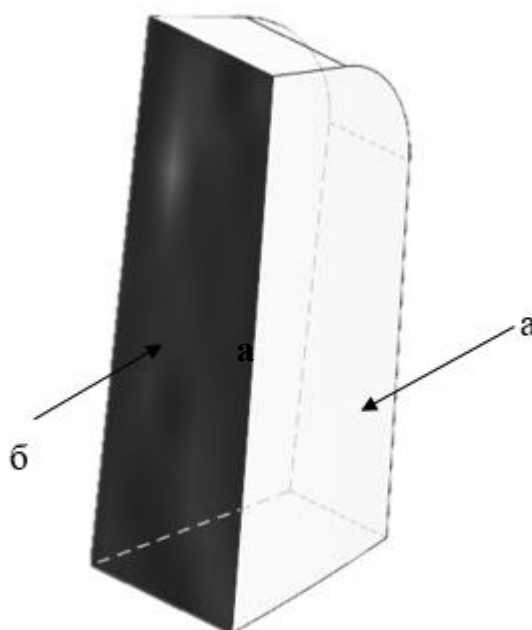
Оброблена пластинка: а – твердий сплав, б – алмазний шар
